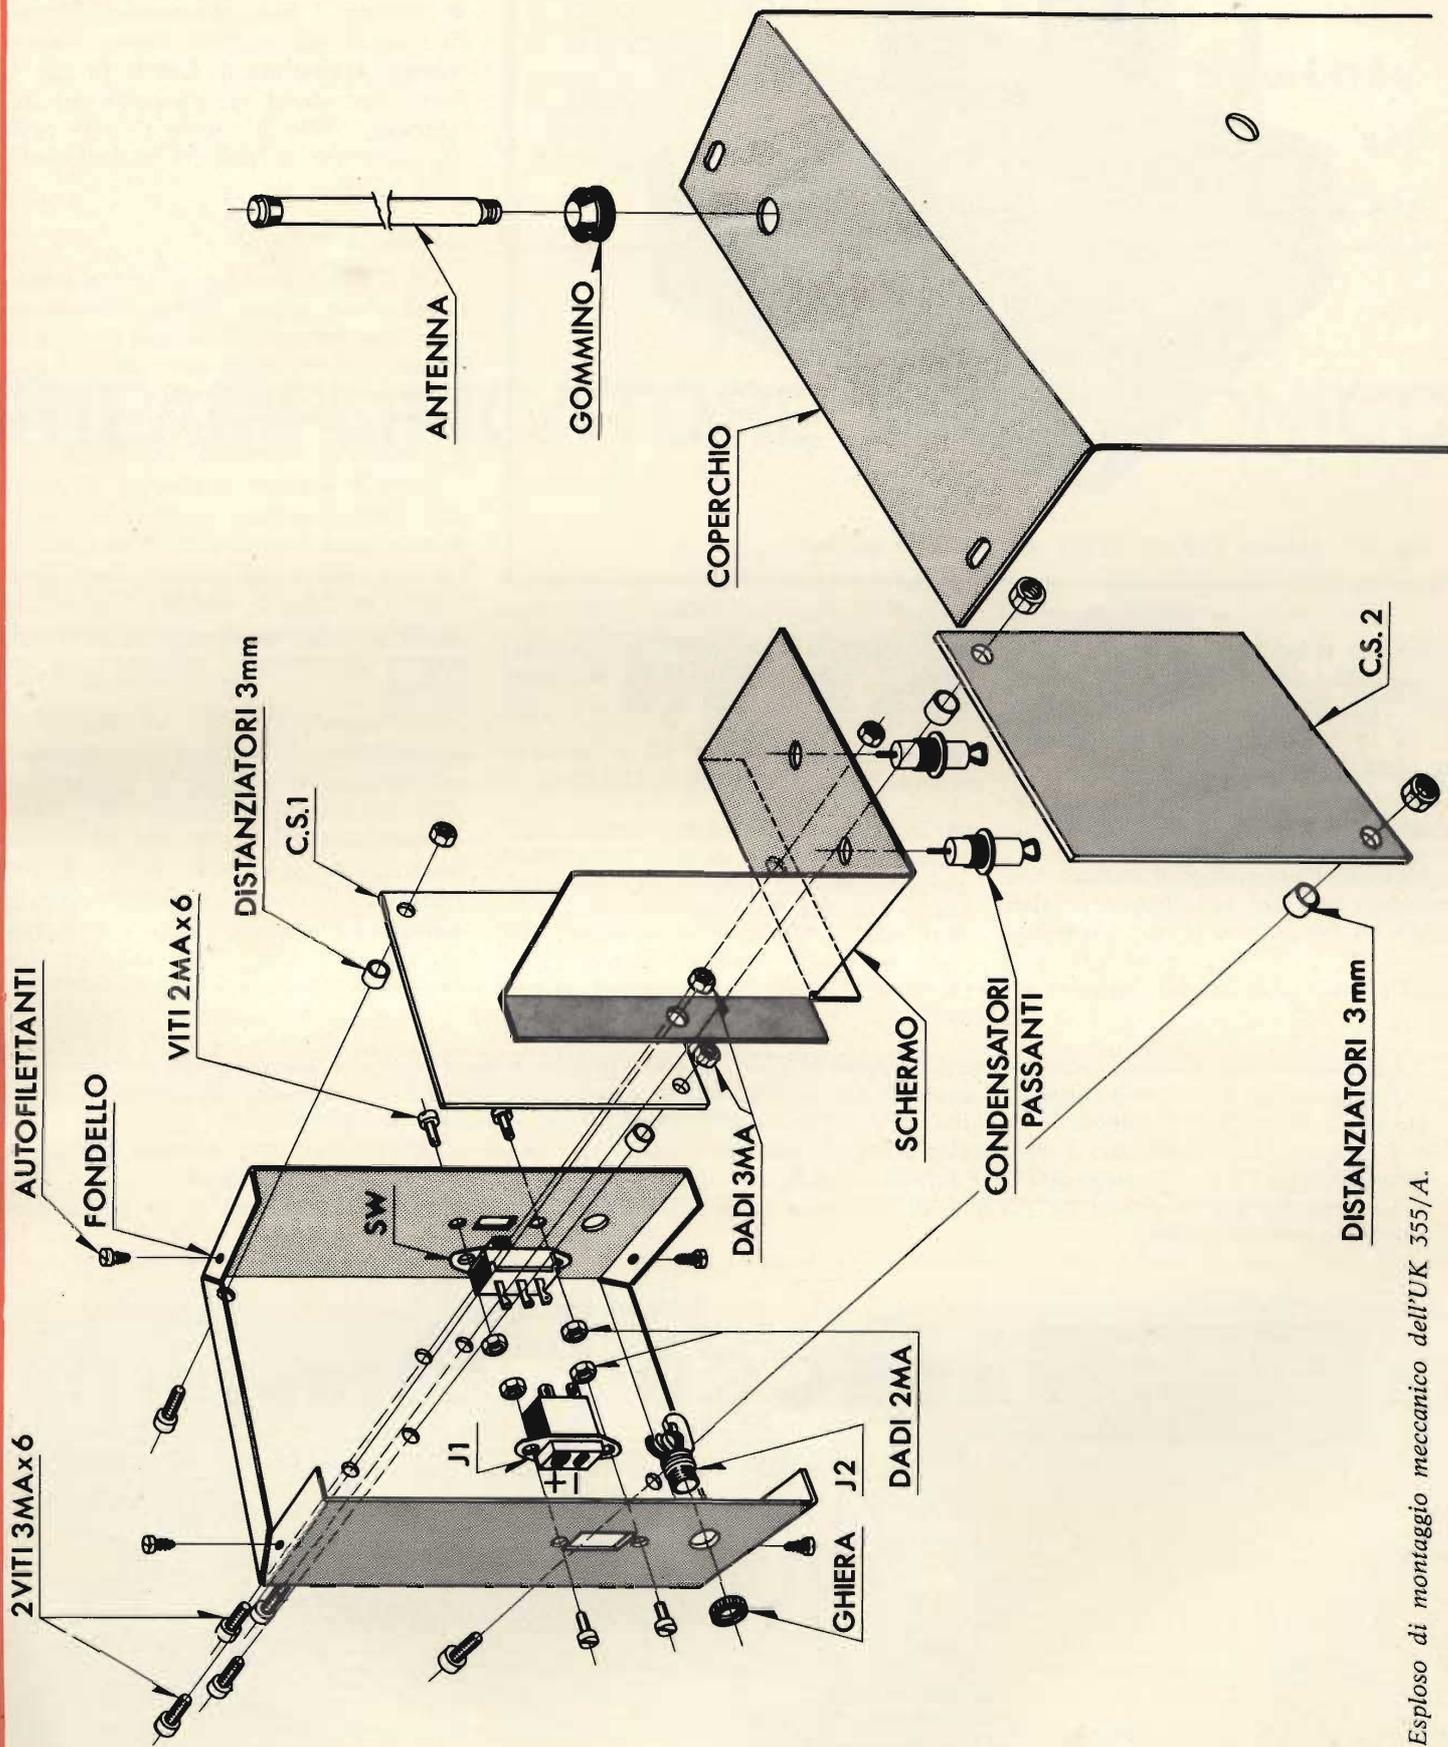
Esploso di montaggio meccanico dell'UK 355/A.
